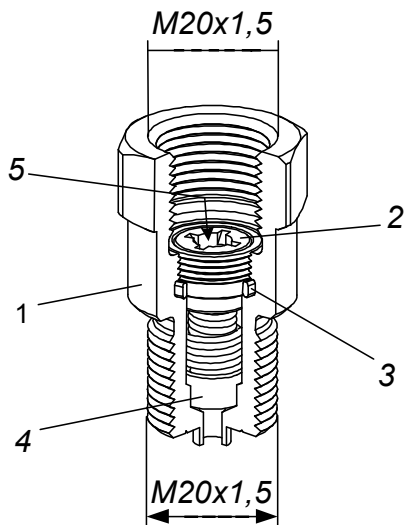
Устройство гасителя колебаний давления ГСК6Мс-1Б1Г: 1 – корпус; 2 – демпфирующая вставка; 3 – уплотнительное кольцо; 4, 5 – фильтр.
